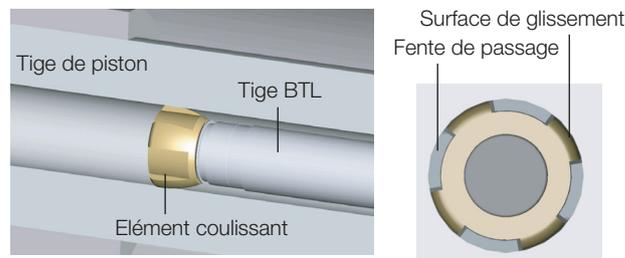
Vue détaillée et vue de dessus de l'élément coulissant
